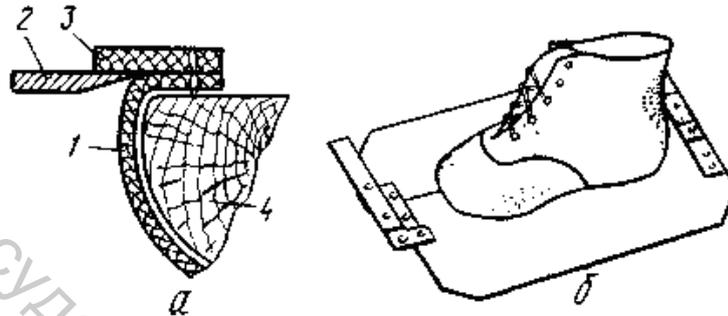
Схема затяжки пластинами (а) заготовки верха обуви методом крепления Парко-1 (б):
